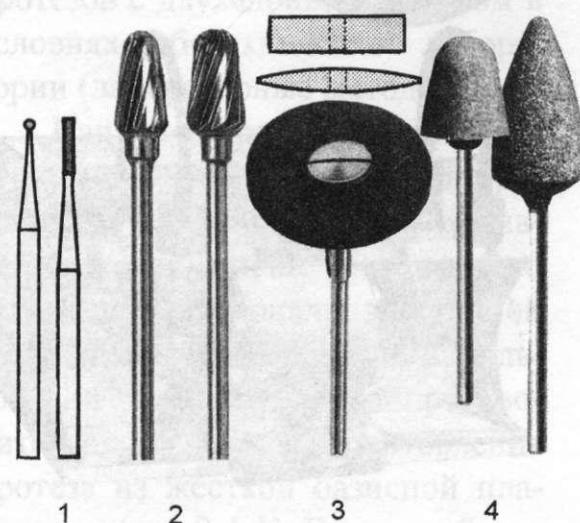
Режущие вращающиеся инструменты для отделки протезов (1 – боры, 2 – фрезы, 3 –шлифовальные круги, 4 – шлифовальные головки).
